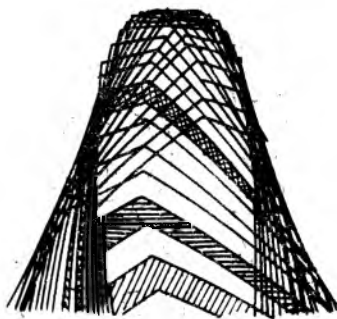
Схема формирования профиля зуба нарезанного колеса при обкатке заготовки с зуборезным долбяком
